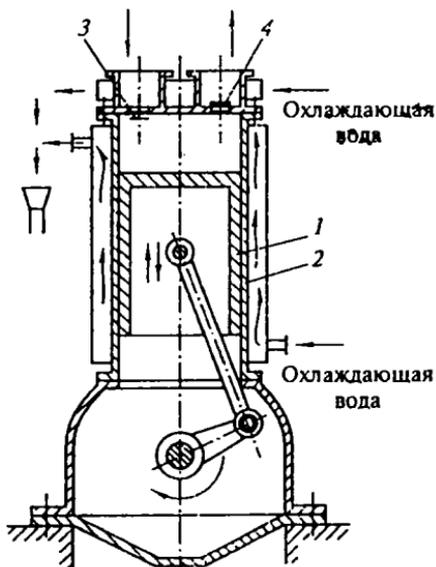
Схема поршневого компрессора с одной ступенью сжатия: 1 — поршень; 2 — цилиндр; 3, 4 — всасывающий и нагнетательный клапаны
